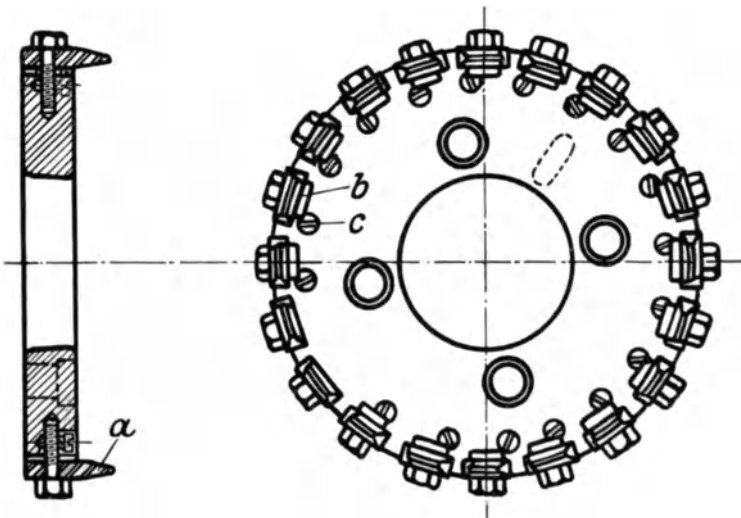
Messerkopf der Gleason Kegelradfräsmaschine.
